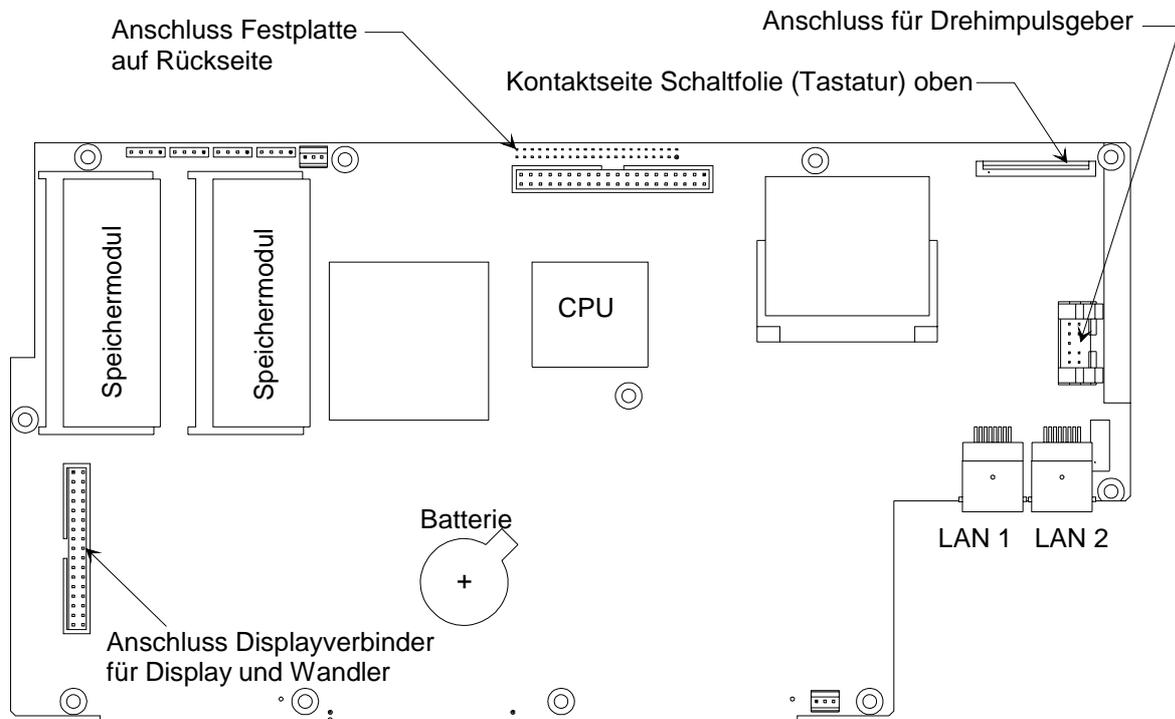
Lage der Steckkontakte auf dem Frontmodulrechner
